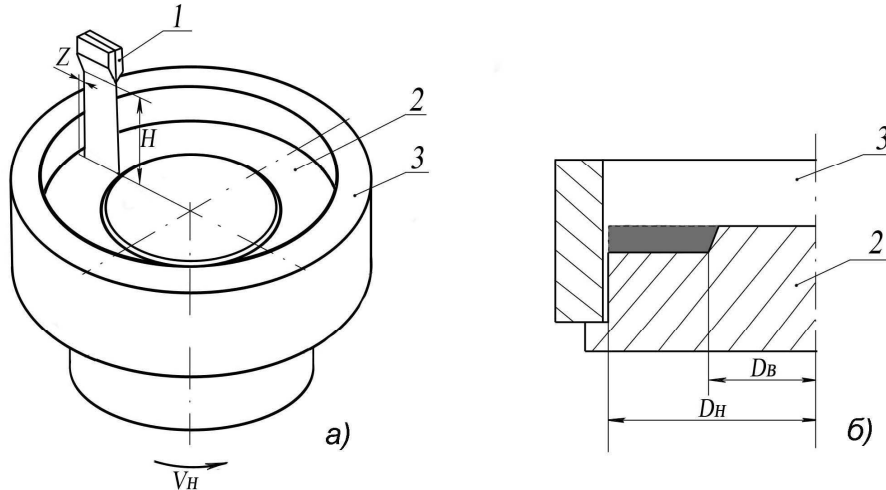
Схема наплавки уплотнительной поверхности задвижек (а) и поперечное сечение наплавляемой детали и формирующего кокиля (б)
